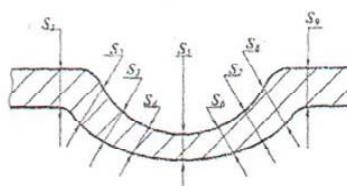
Схема замірів мікротвердості і товщини стінки корпуса в зоні кільцевої канавки
